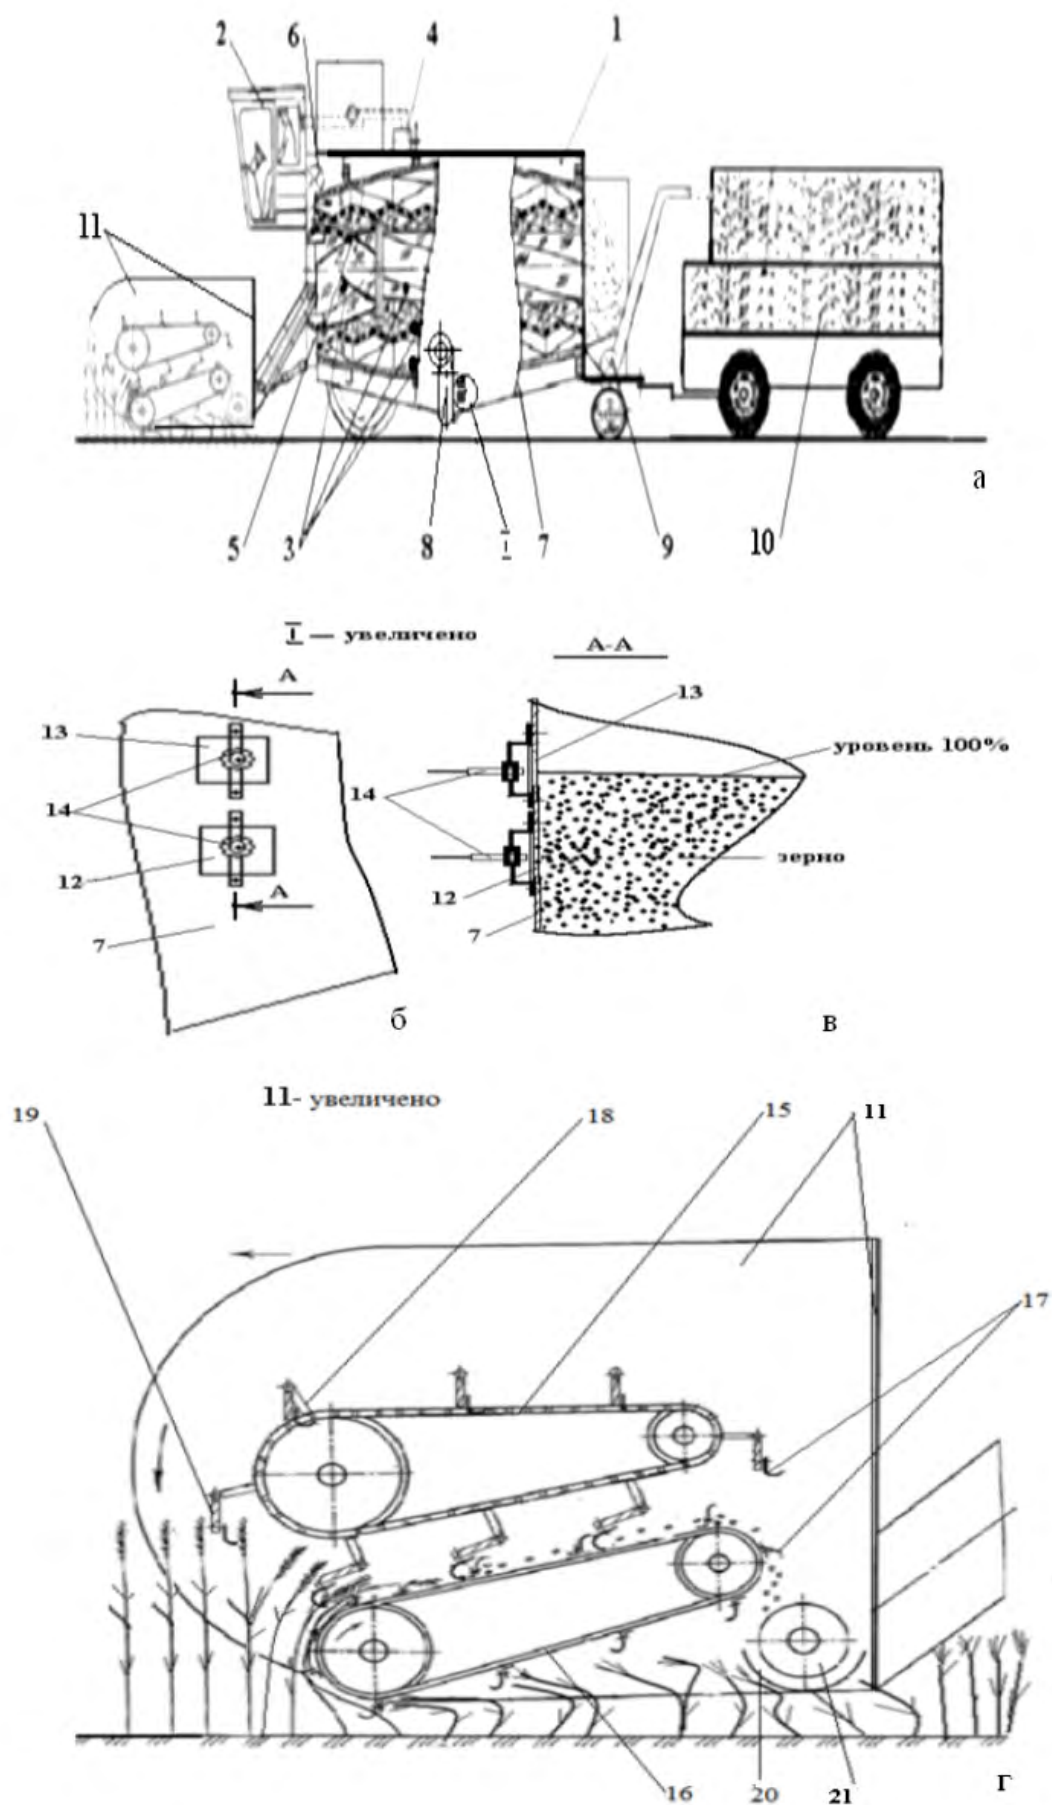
Схема прямооточного зерноуборочного комбайна: а – вид сбоку агрегата; б, в – места установки датчиков; г – очесывающая жатка (обозначения в тексте)
